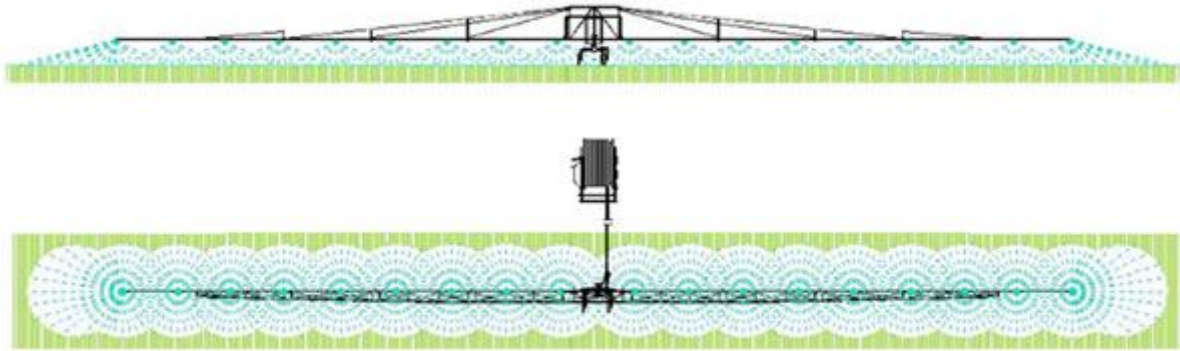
Конструктивная схема элементы крепления консоли – Spray Boom
